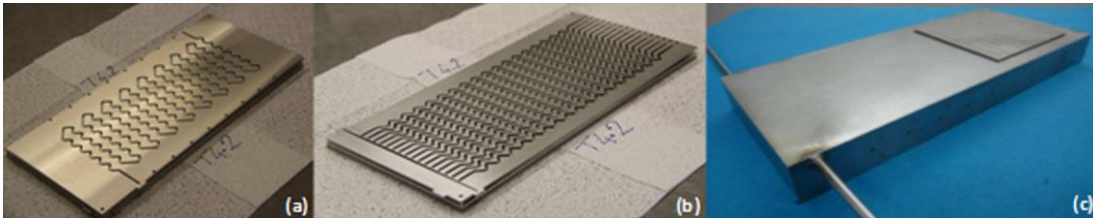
(a) Plaque procédé ; (b) Plaque utilité ; (c) l'échangeur /réacteur après assemblage [32].
